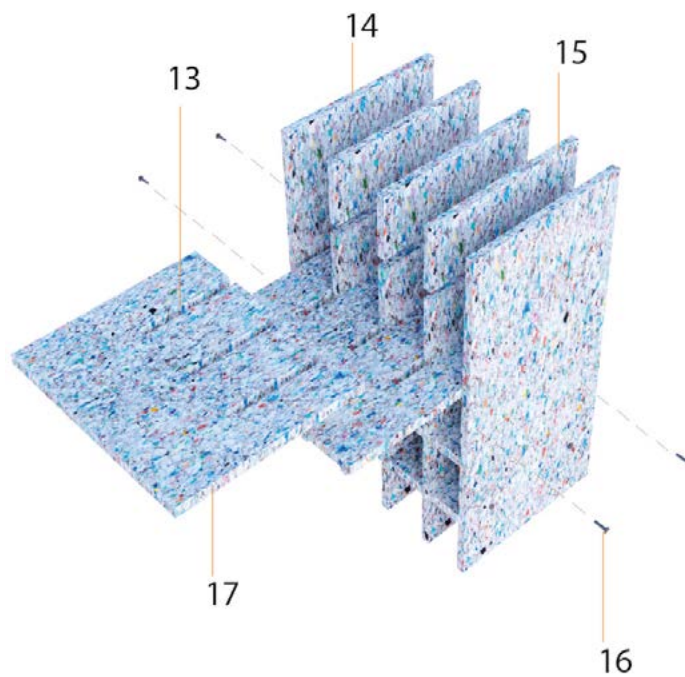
Detalle constructivo 3d vinera HDPE reciclado
